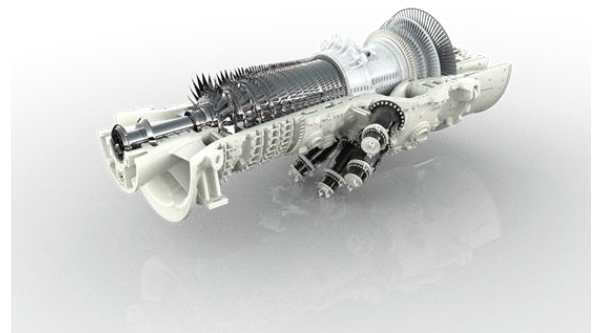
GT36 Maschinenansicht (geöffnet)
